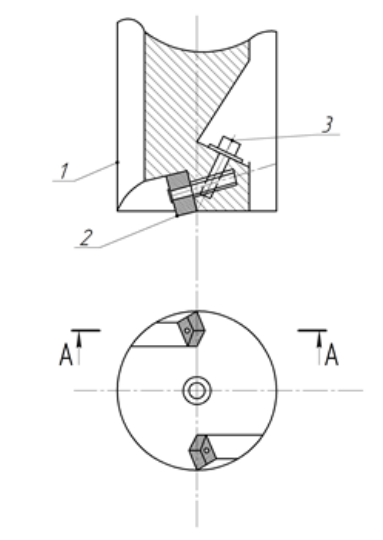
Сборный зенкер: 1-корпус зенкера, 2-режущая пластина, 3-затяжная гайка
